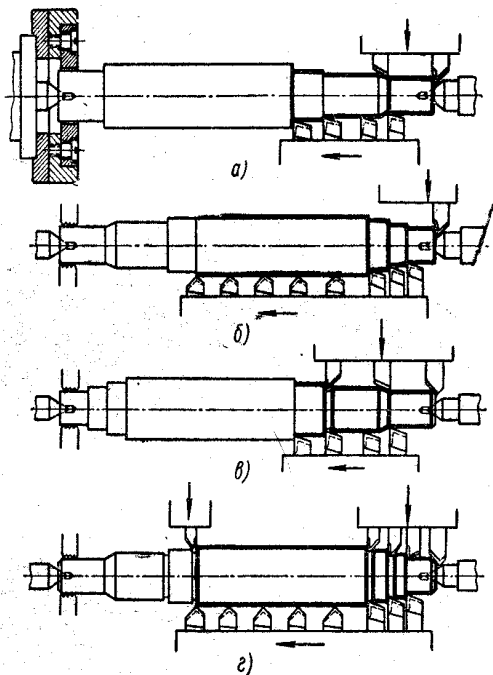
Схема обточування заготовки на багаторізцовому напівавтоматі:
